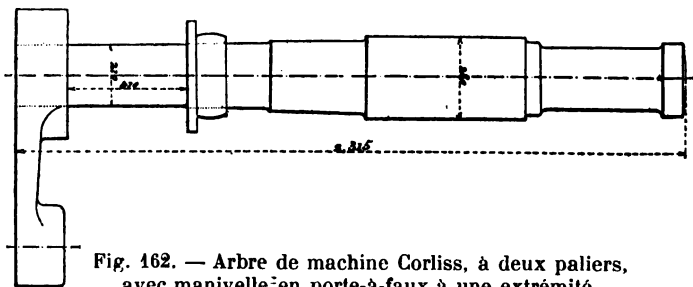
Arbre de machine Corliss, à deux paliers, avec manivelle en porte-à-faux à une extrémité.
